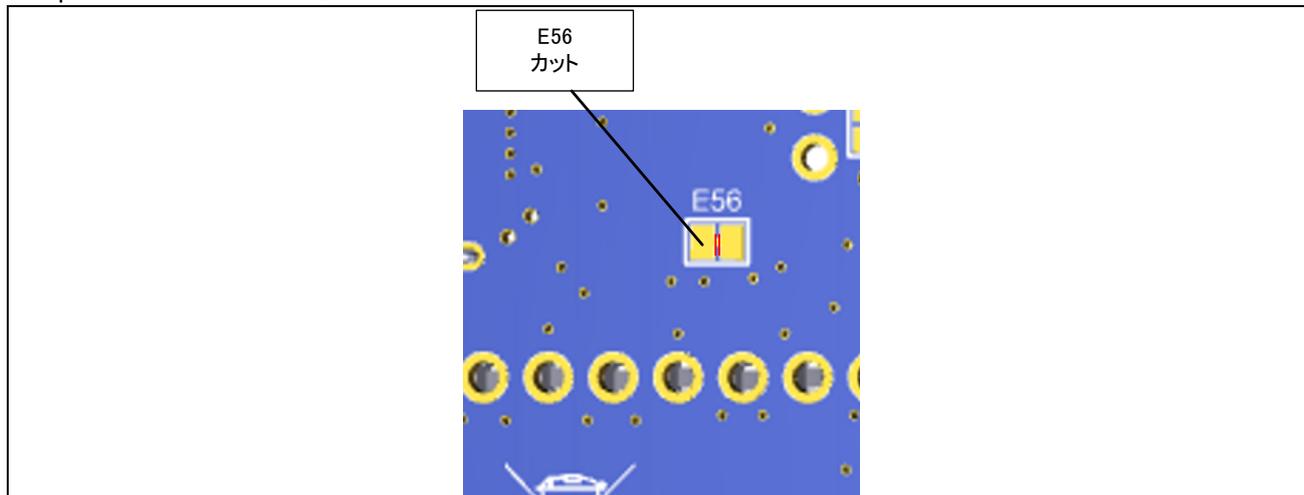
Jumper Trace Cut E56 位置(はんだ面)
